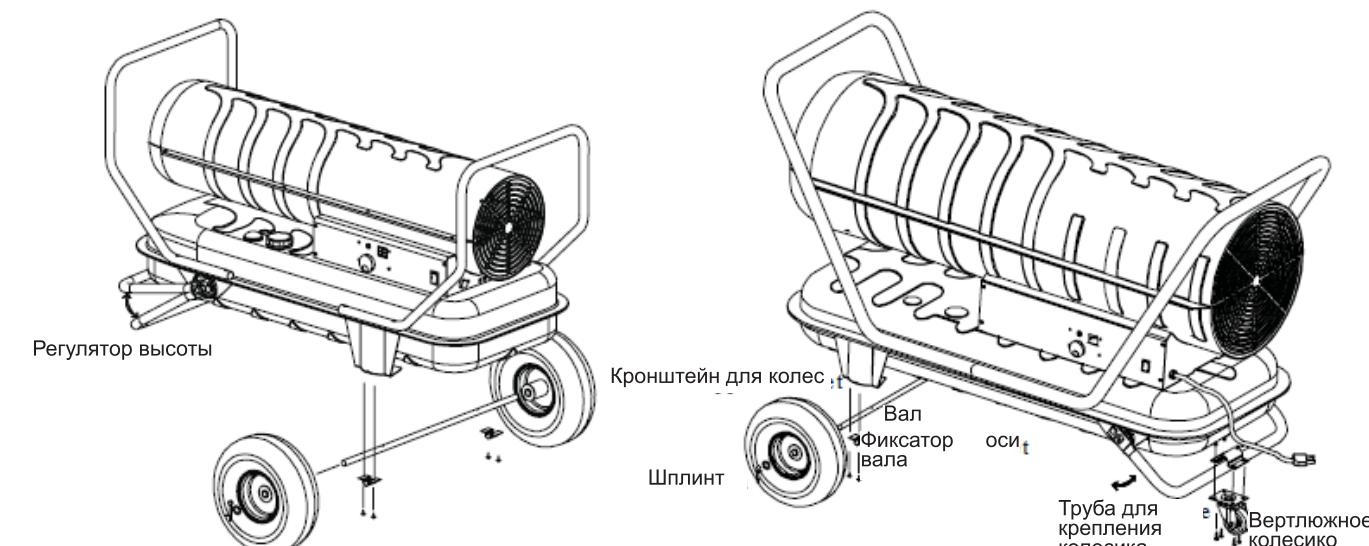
Сборка нагревателей моделей TK-50000,TK-70000, TK-100000
